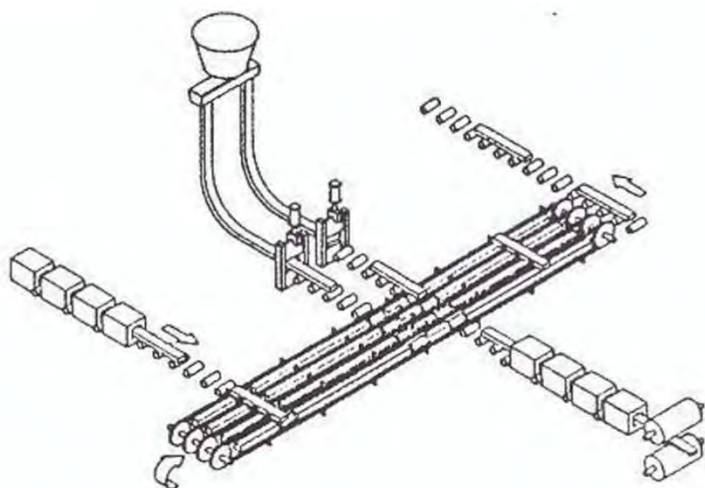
Схема литейно-прокатного агрегата с индукционным нагревом заготовок, предусматривающая и прямой, и повторный нагрев их заготовок с промежуточного склада
